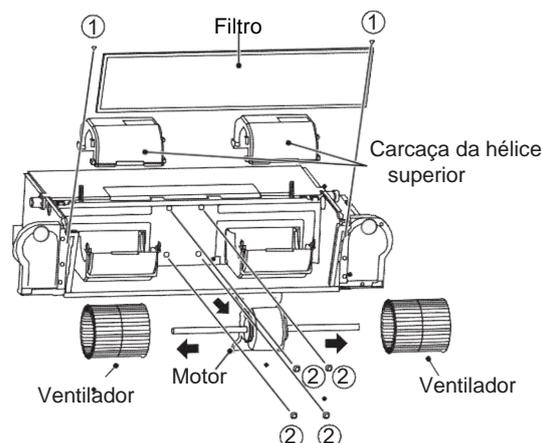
Remoção do filtro, tampa superior e parafusos do motor
